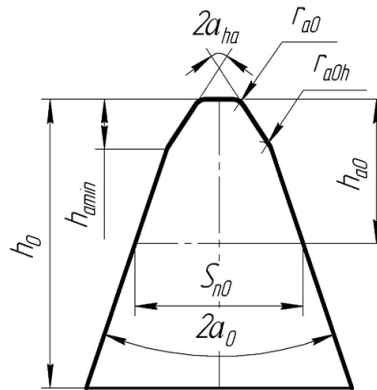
Профіль зуба фрези, що дозволяє виключити особливу точку на поверхні зубчастого колеса, що обробляється [2].
